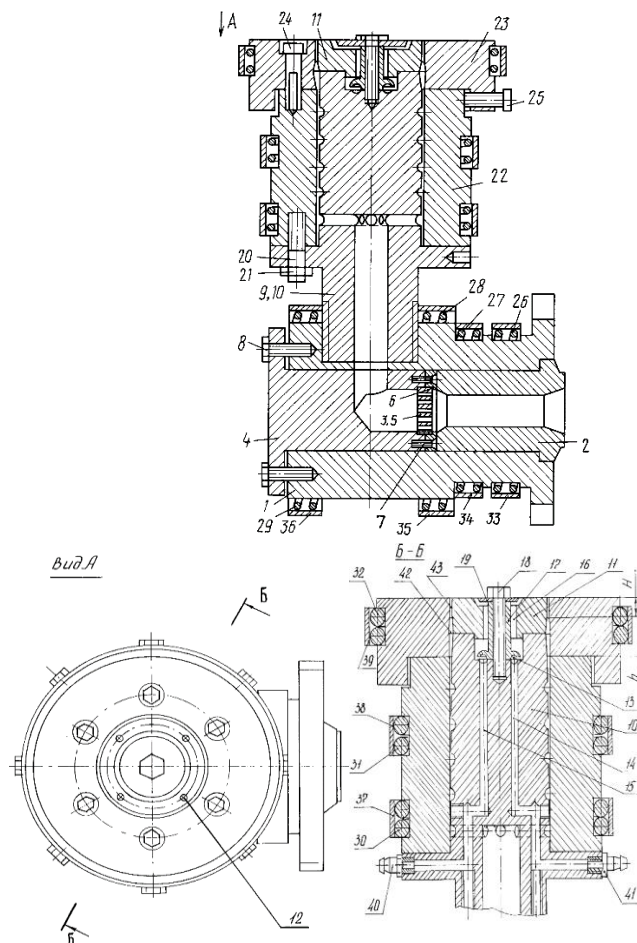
Екструзійна головка для виготовлення рукавної плівки з канавками в дорні
